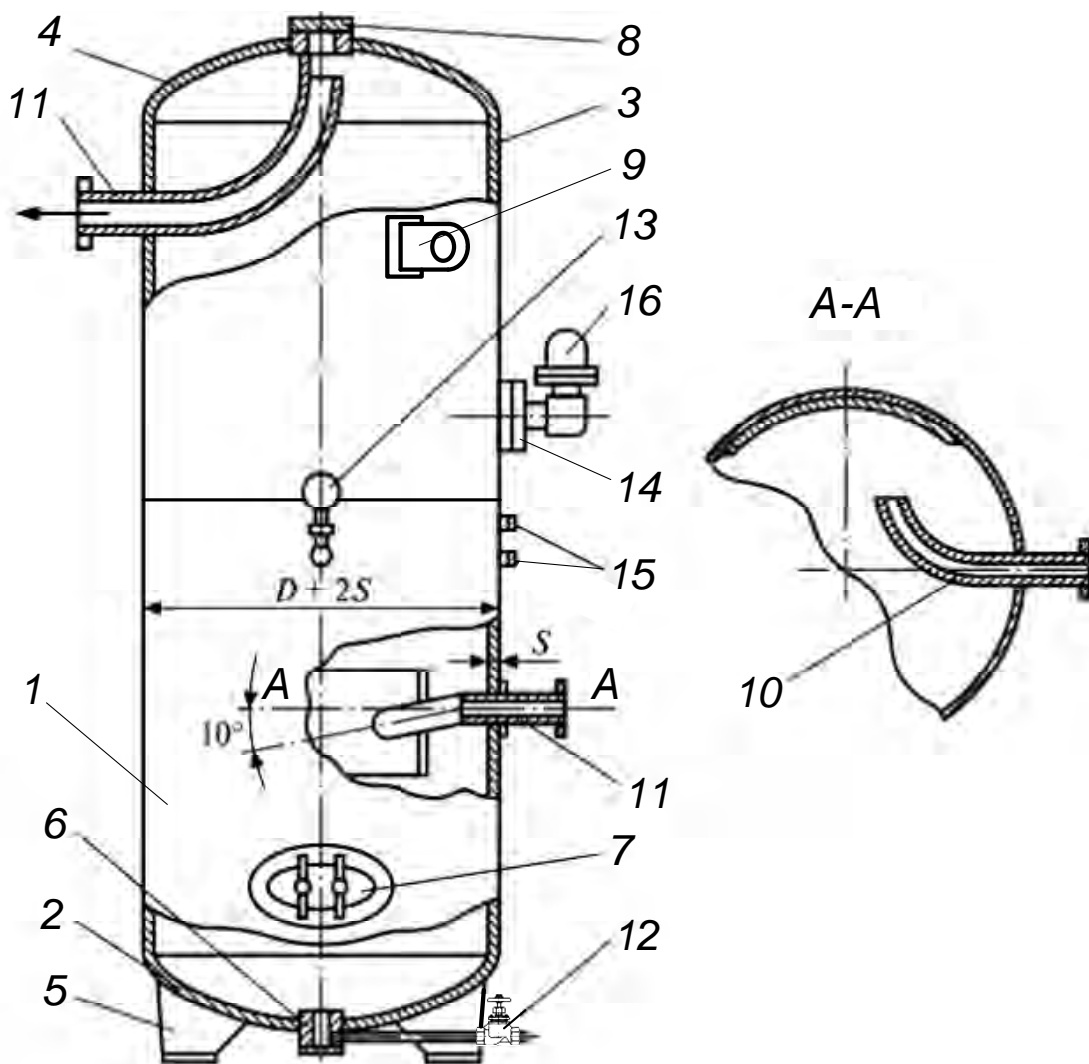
Воздухосборник В-2: 1 – нижняя обечайка; 2, 4 – эллиптические днища; 3 – верхняя обечайка; 5 – опора; 6 – люк; 7 – крышка люк-лаза; 8 – технологический люк; 9 – строповочное устройство; 10 – труба; 11 – патрубок; 12 – вентиль; 13 – манометр; 14 – фланец; 15 – штуцер к регулятору производительности и к манометру в машинном отделении; 16 – предохранительный клапан
